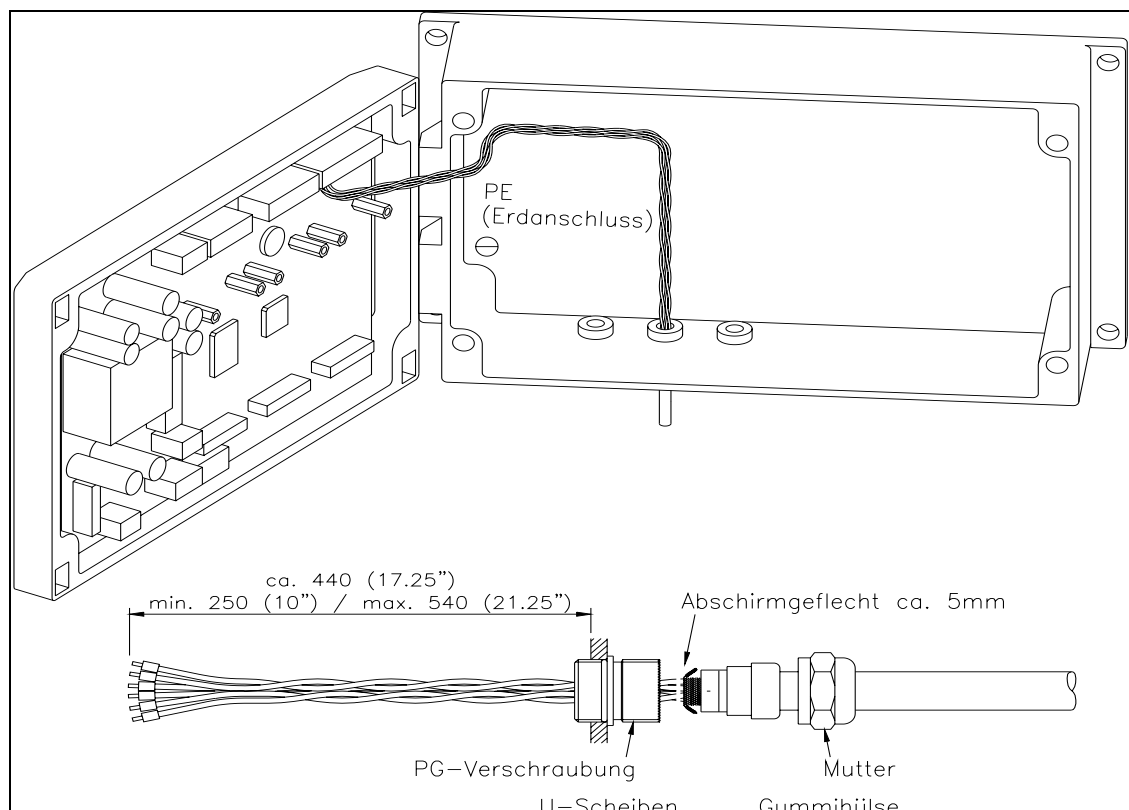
Verlauf der Anschlusskabel im Gehäuse
